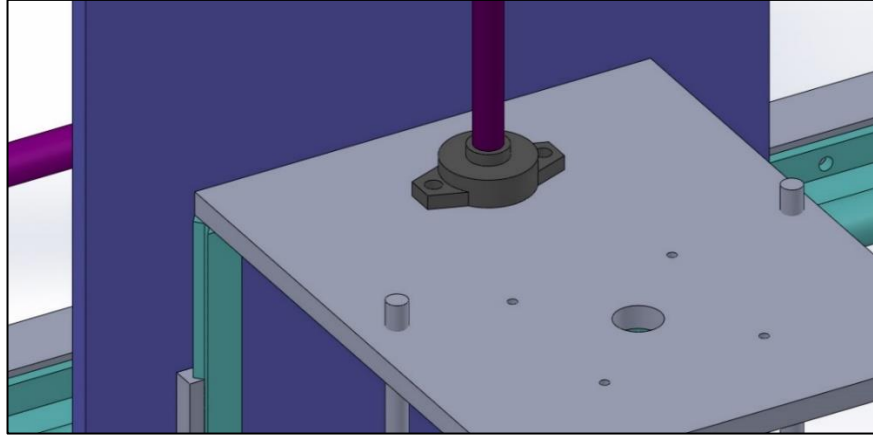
Z eksen motor ve vidalı mil şasisi montajı
